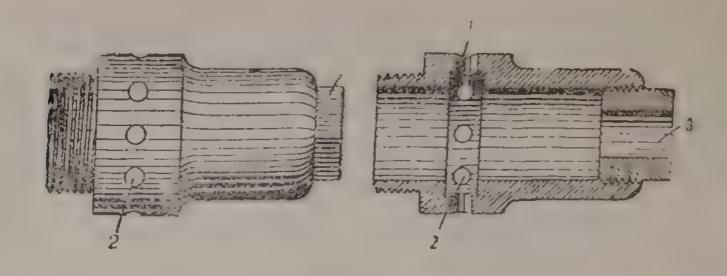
Надульник: 1 — кольцесбразный паз; 2 — отверстия; 3 — вгулка; 4 — напал
